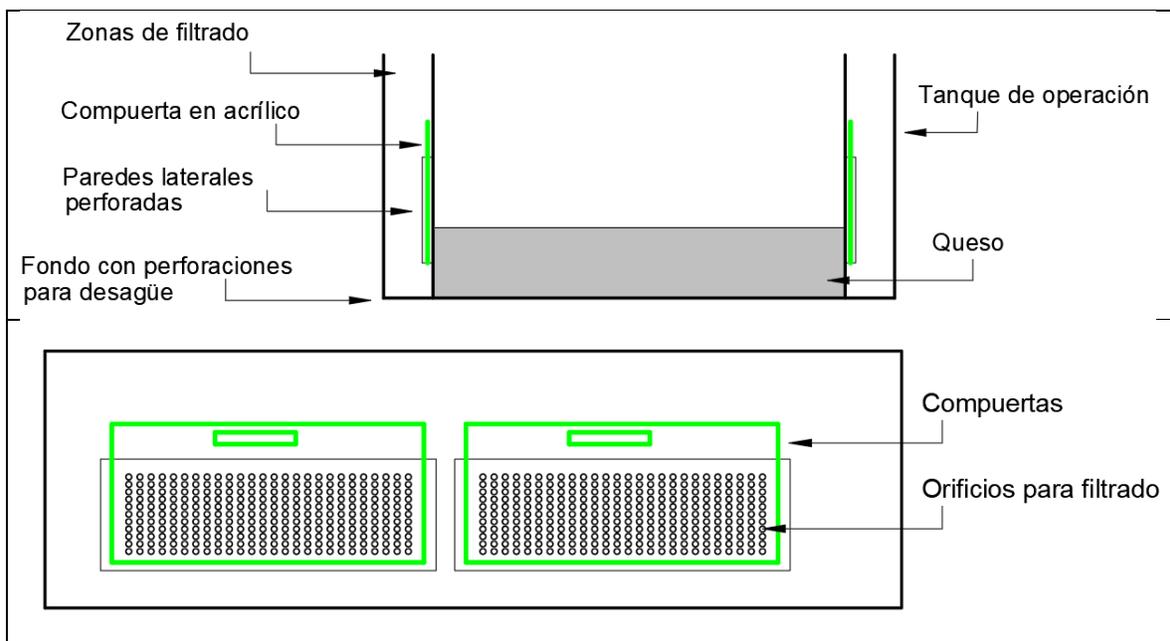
Dibujos de ingeniería de detalles, corte transversal y longitudinal del tanque de operación.
